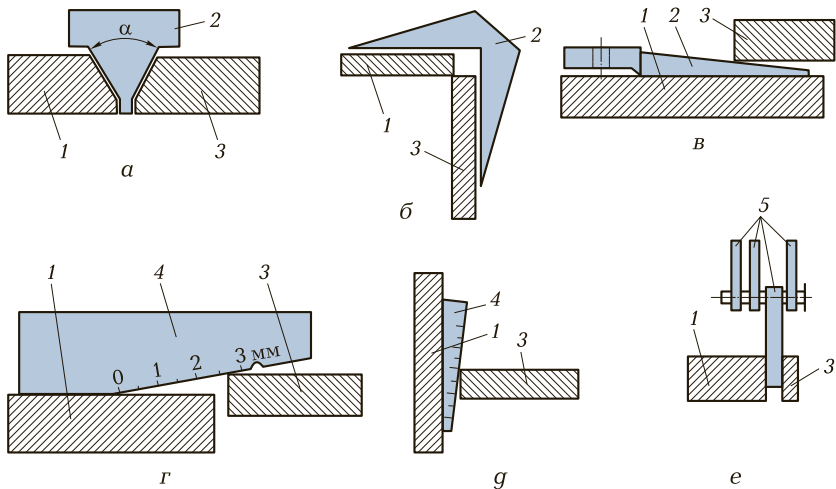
Контроль качества сборки деталей к сварке с использованием:
